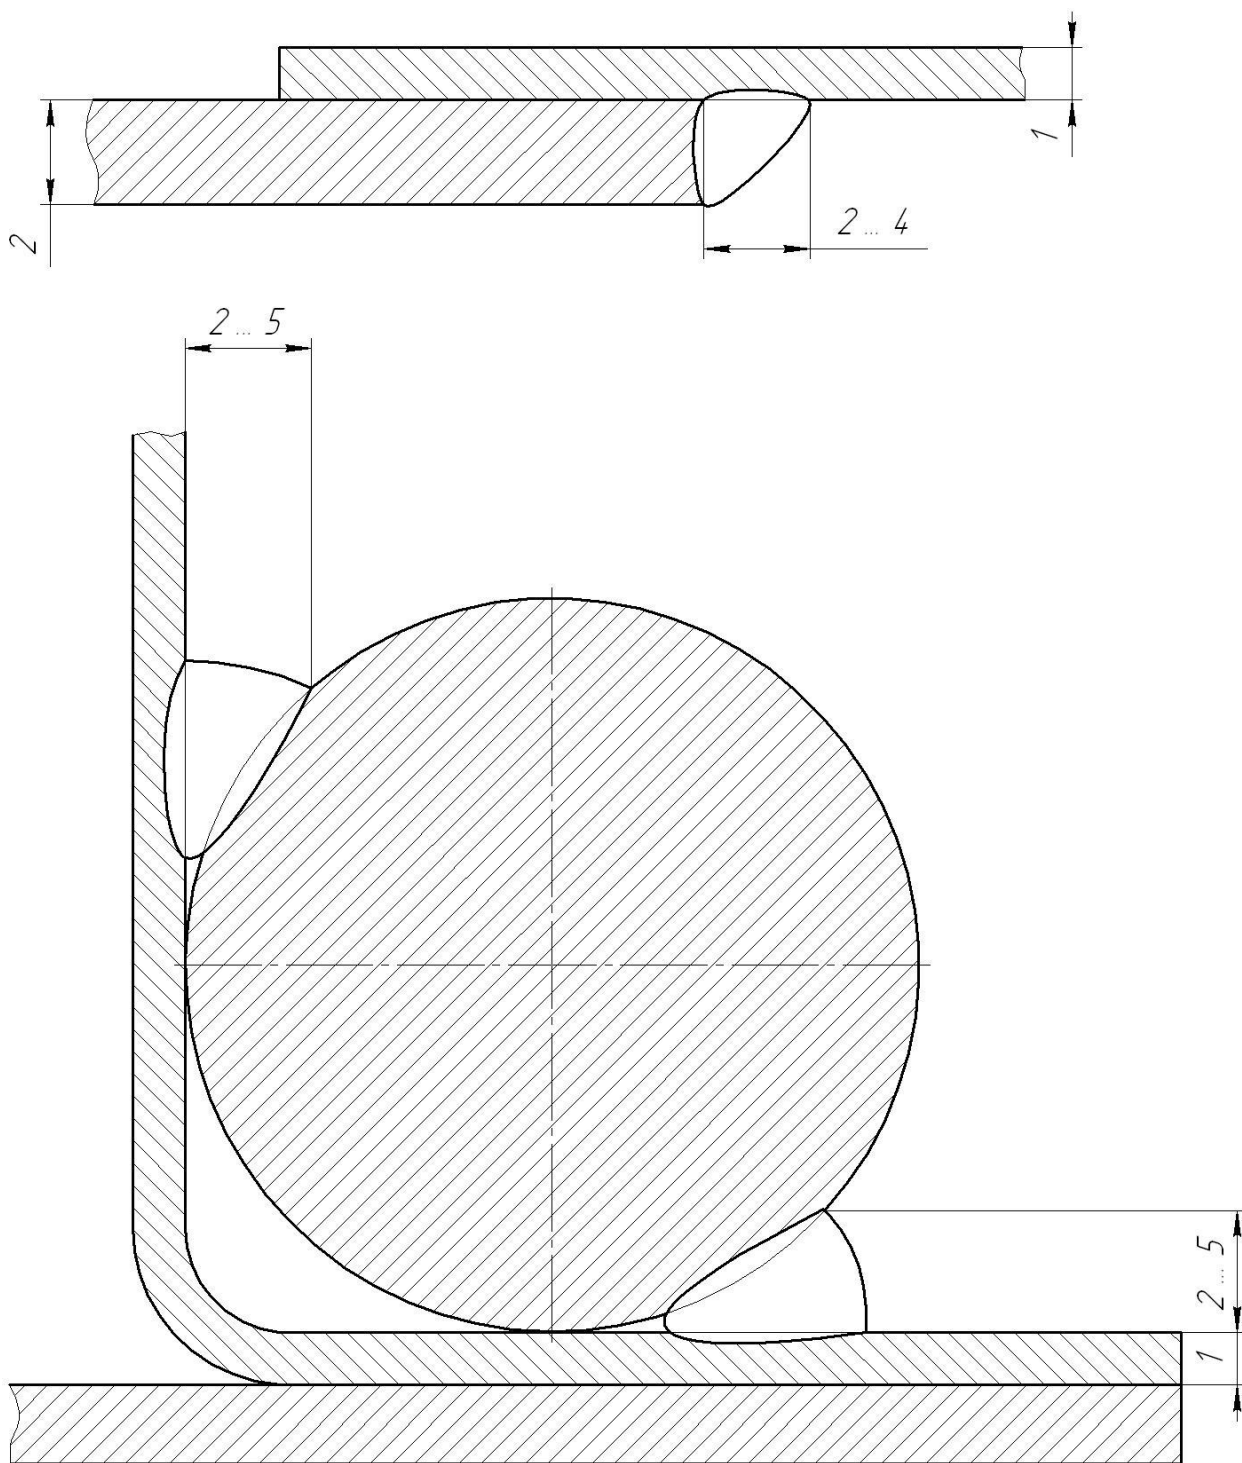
Геометрические размеры соединений дуговой сварки
